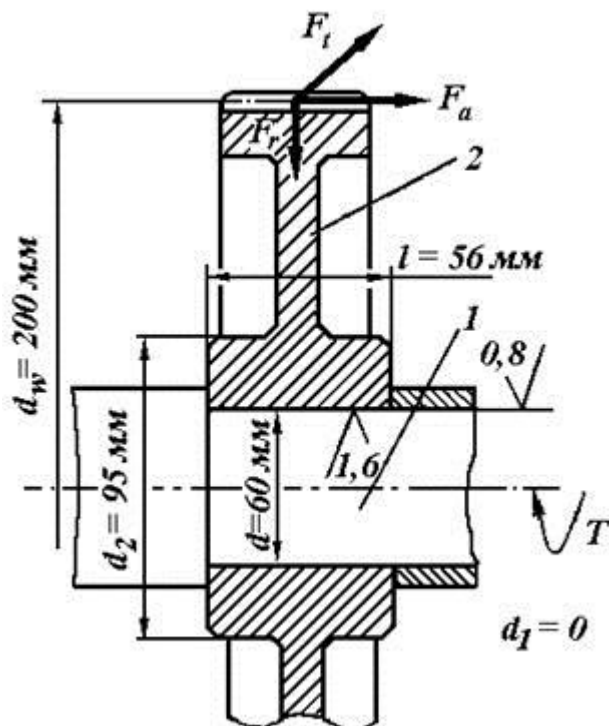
Зубчатое колесо, установленное на вал запрессовкой
